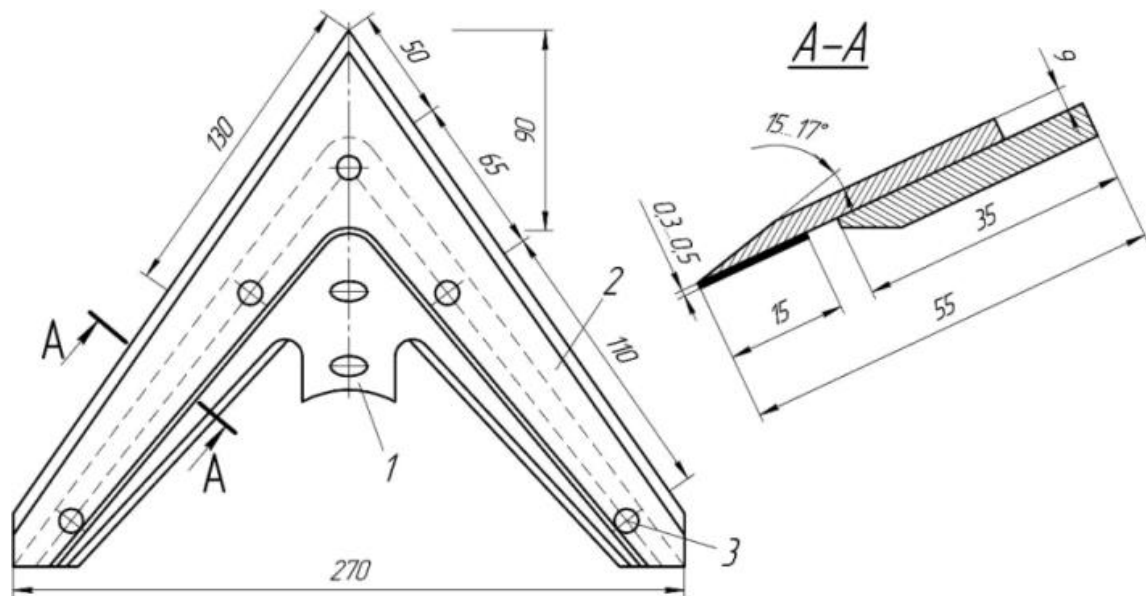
Культиваторна лапа складальної будови, розробник Канівець І.Д.: 1 – корпус; 2 – змінне лезо; 3 – заклепки
